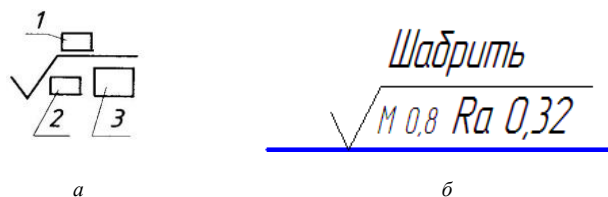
Обозначение шероховатости: *a* – структура (*1* – способ обработки; *2* – условное обозначение направления неровностей и базовая длина; *3* – буквенный параметр шероховатости и его величина в мкм); *б* – пример простановки шероховатости поверхности на чертеже
